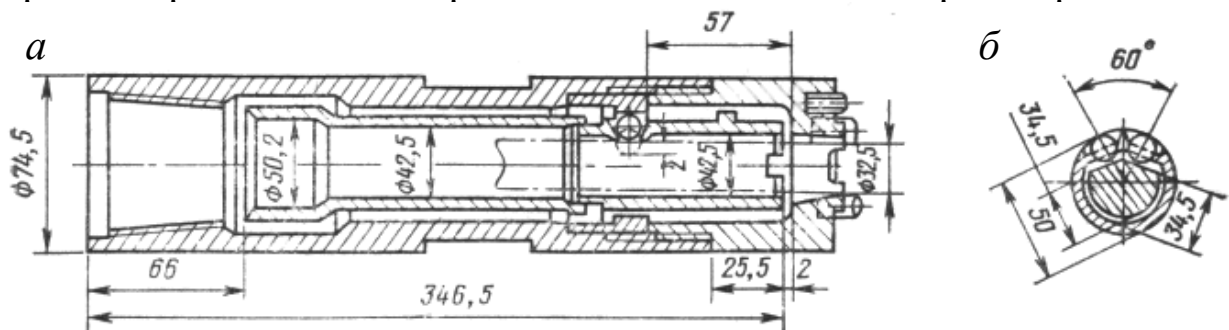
Конструкция кернолома (а) и схема опрессовки шариков (б)
